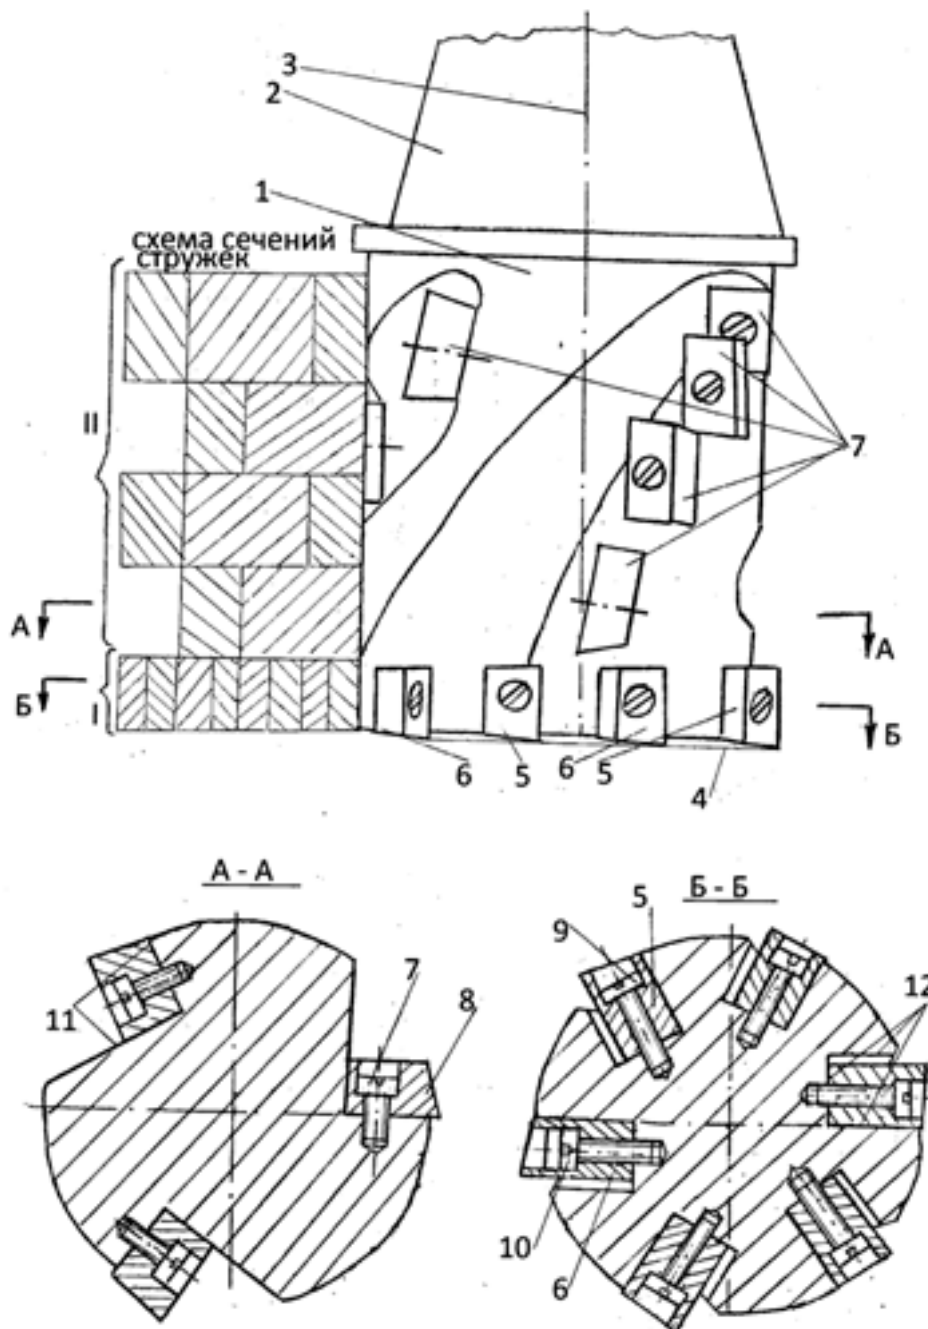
Торцово-цилиндрическая фреза с дополнительными торцовыми пластинами в торцовой части
